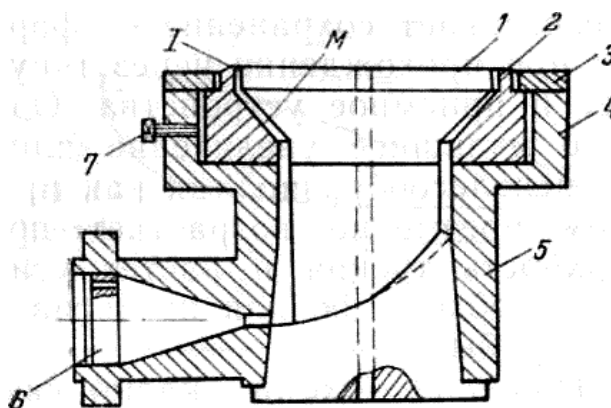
Схема кутової головки з боковим введенням розплаву: 1 – дорн; 2 – матриця; 3 – кільце; 4 – корпус; 5 – дорноутримувач; 6 – решітка; 7 – регульовальні гвинти; Т – формуючий зазор; М – дифузорний канал
